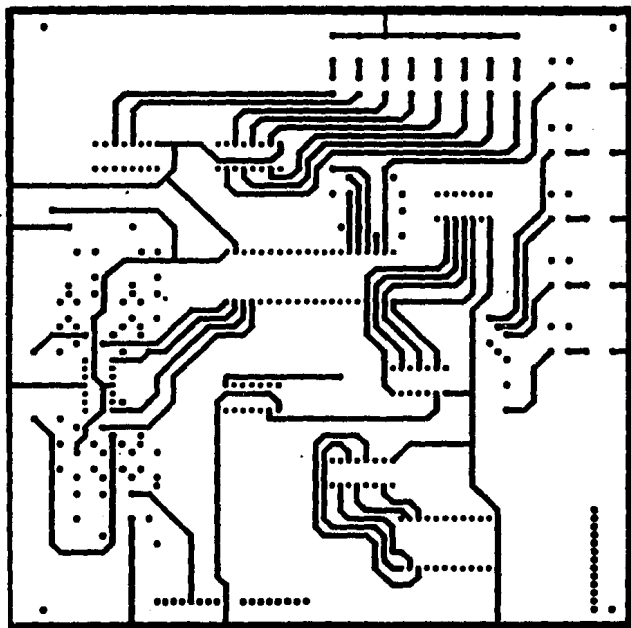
DIAGRAMA DEL LADO DE SOLDADO DE SOLDADO
